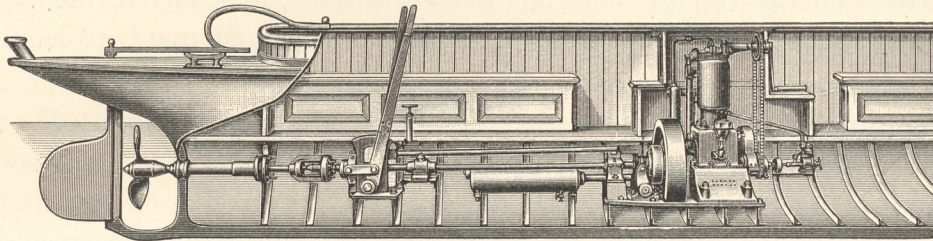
Maschinenanlage mit Otto-Motor und Meißners Umsteuerschraube.
